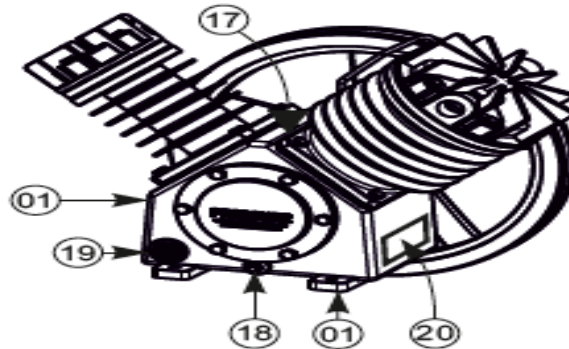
Partes que componen un Compresor Alternativo Lubricado
